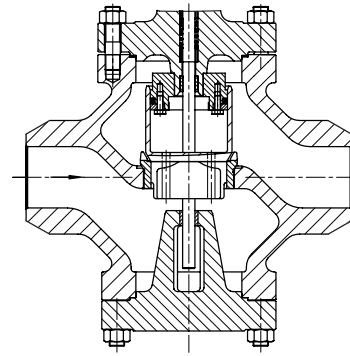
· Valvola Tipo 3254 con attacchi a saldare ed otturatore bilanciato
